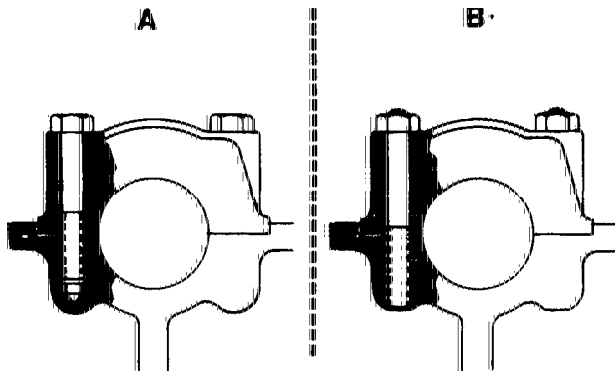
Болты и крышка коренного подшипника старого (А) и нового (В) типов.
